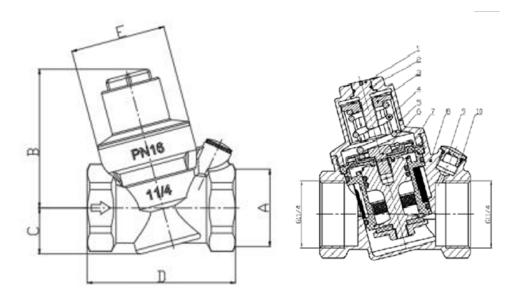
Устройство и габаритные размеры редукционного клапана ДУ 32
